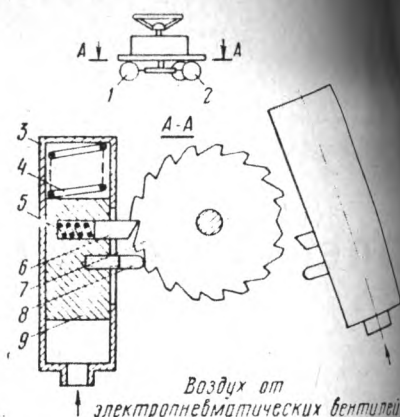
Пневматический привод контроллера: 1, 2 — цилиндры набора и сброса; 3 — корпус цилиндра; 4, 5 — пружины; 6, 8 — упоры; 7 — храповик; 9 — поршень
